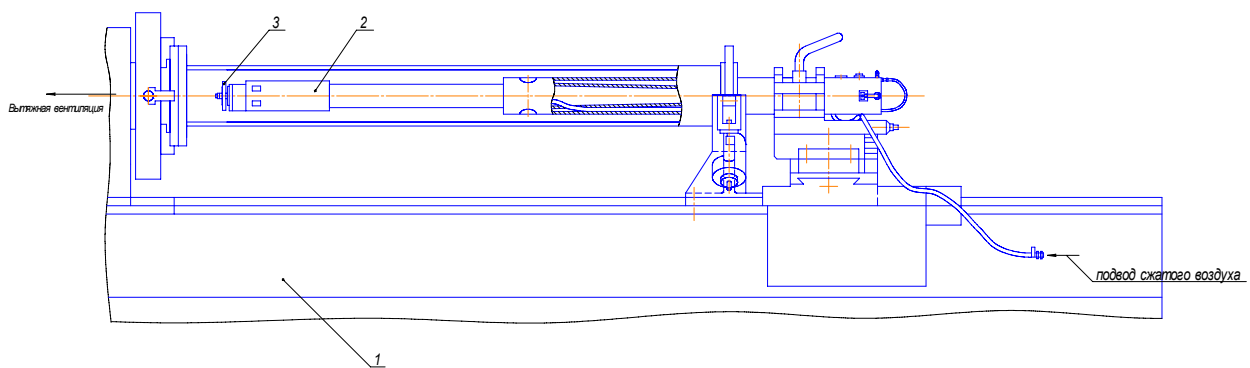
Схема обработки корпуса: 1 – станок модели 1К62; 2 – установка для обработки и удаления покрытий; 3 – абразивный инструмент
